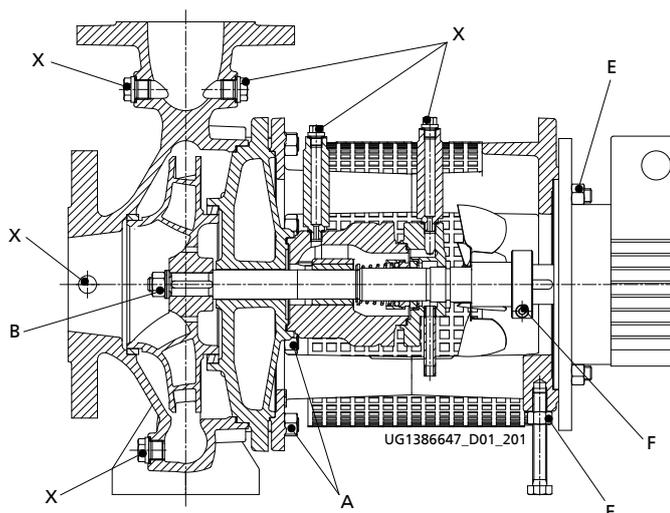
Posiciones de apriete de los tornillos de la bomba
